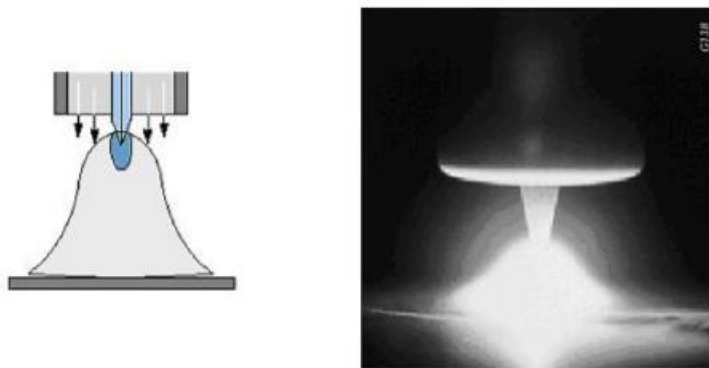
Imagen termométrica del proceso de soldadura GTAW.
